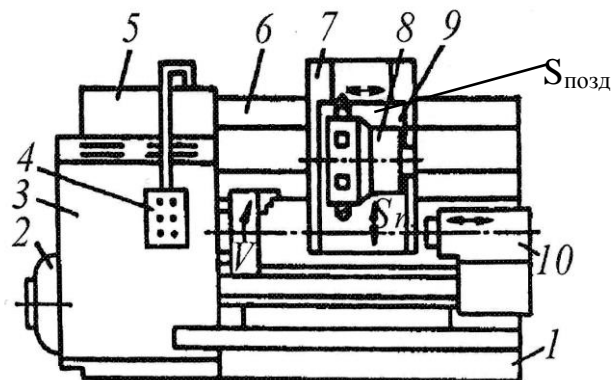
Загальний вид токарно-гвинторізного верстата з ЧПК
